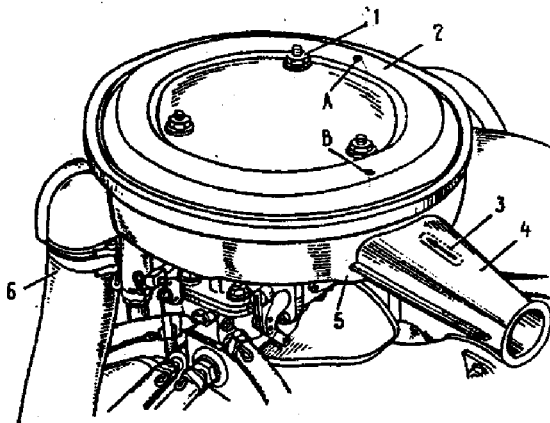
Conjunto do filtro de ar: 1 - porca de fixação; 2 - tampa do filtro; 3 - seta reguladora; 4 - tomada de ar para temperaturas altas; 5 - carcaça do filtro; 6 - mangueira de tomada de ar para baixas temperaturas; A - marca azul - quente; B - marca vermelha - frio.
